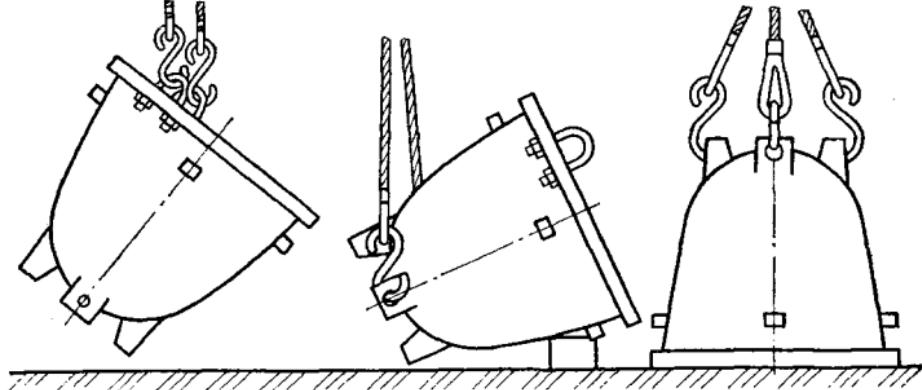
Кантовка корпуса в вертикальной плоскости на 180° для установки на расточкой станок
